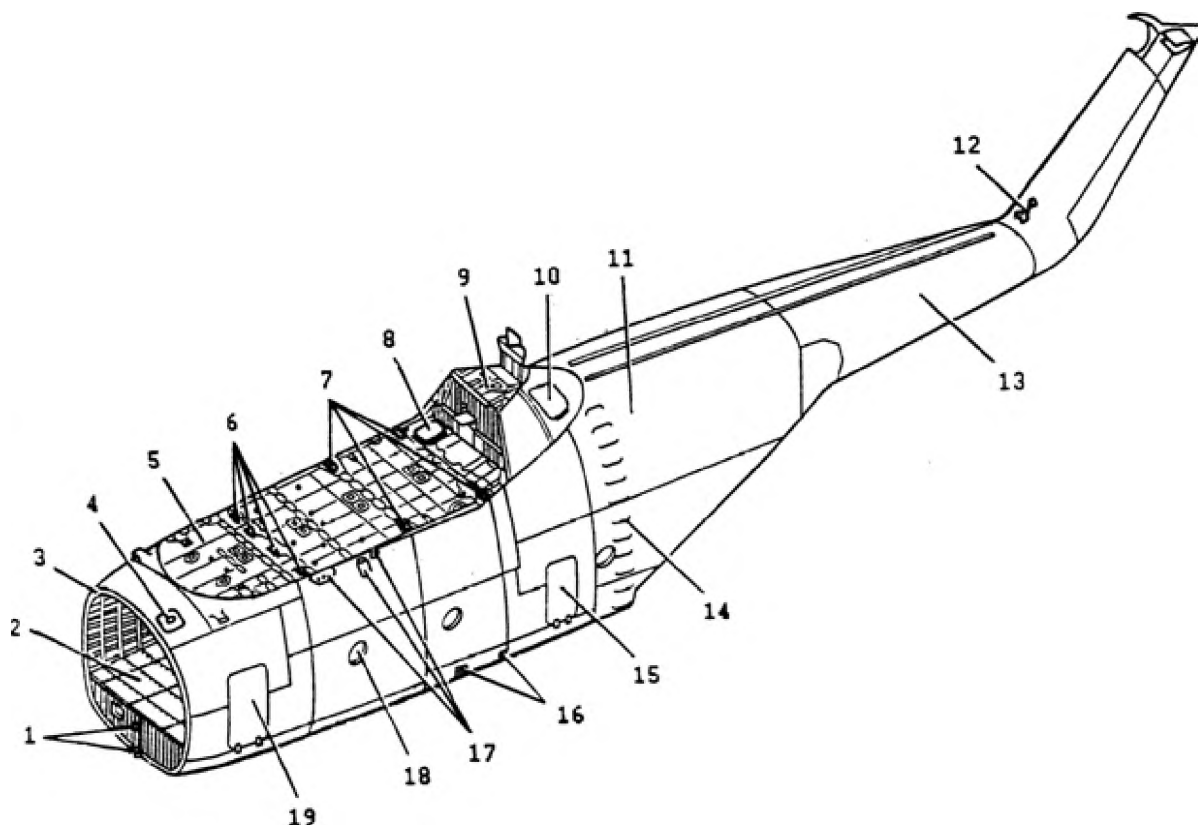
Конструкция центральной части фюзеляжа с хвостовой балкой вертолета Ми-26[9]:
